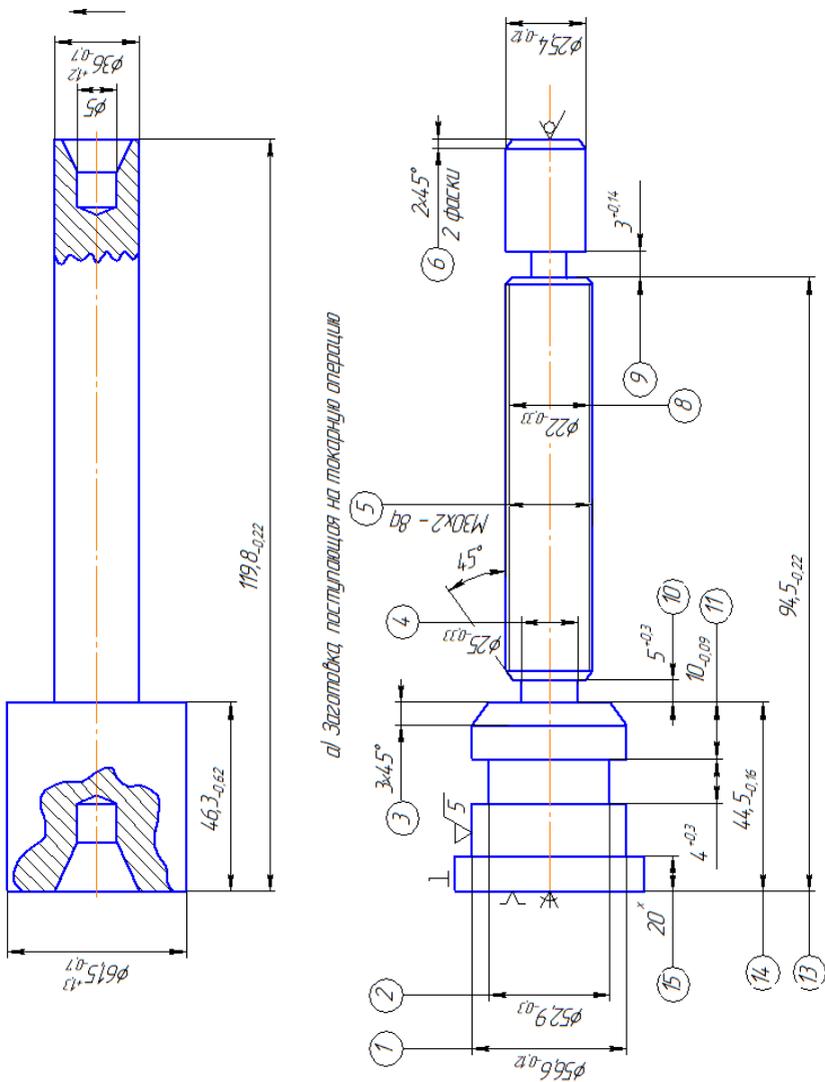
Эскизы заготовки и токарной операции обработки детали «Вал»
